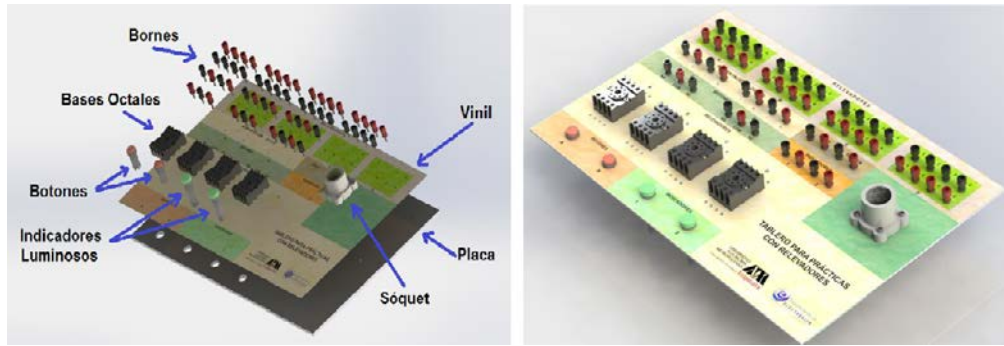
Vistas en explosión y de ensamble de la placa superior del prototipo.
